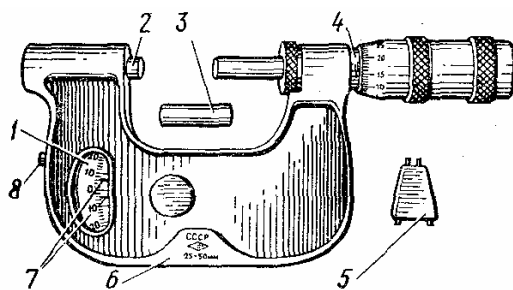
Микрометр рычажный: 1 – шкала; 2 – подвижная пятка; 3 – установочная мера; 4 – микрометрическая головка; 5 – ключ; 6 – скоба; 7 – указатели пределов поля допуска; 8 – кнопка отвода подвижной пятки
